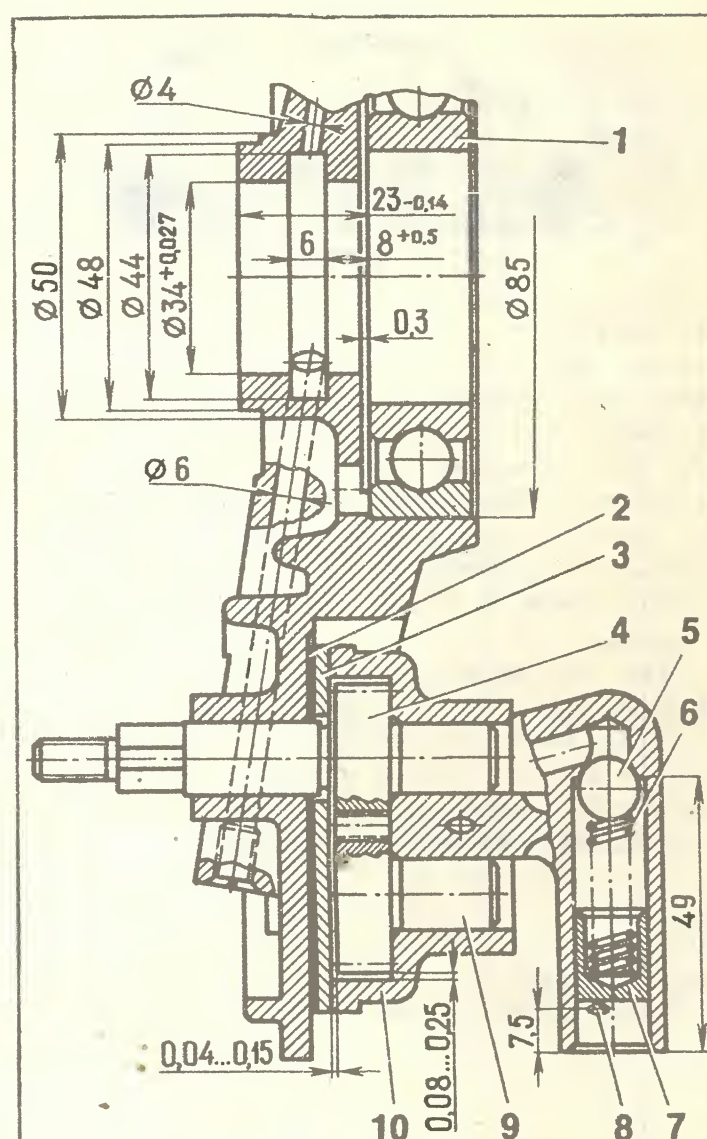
Корпус переднего подшипника коленчатого вала и масляный насос: 1 — подшипник; 2 — прокладка; 3 — крышка; 4 — ведущая шестерня насоса; 5 — шарик (диаметр 10 мм) редукционного клапана; 6 — пружина; 7 — пробка; 8 — шплинт; 9 — ведомая шестерня; 10 — корпус масляного насоса.
